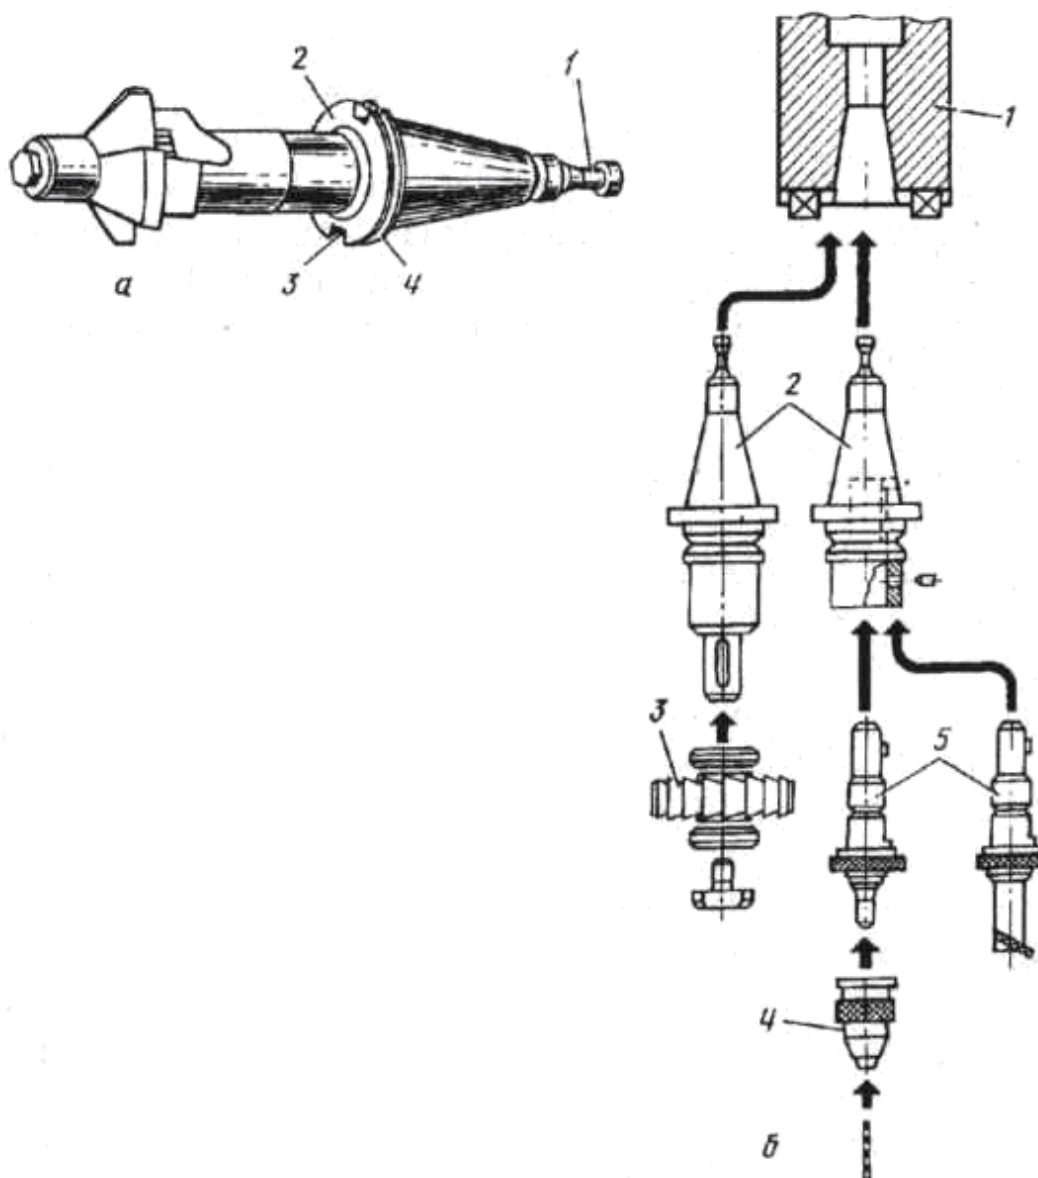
Схема побудови інструментального комплексу для багатоцільових верстатів: а – інструментальна оправка з конічним хвостовиком; б – загальна схема комплексу
